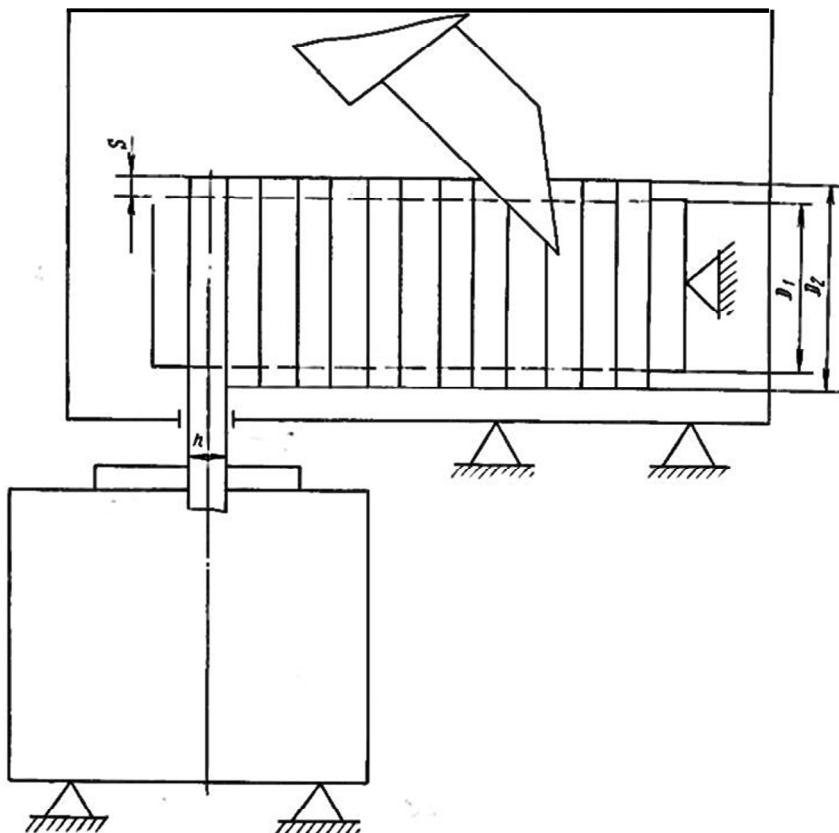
Схема изготовления разрезных колец из полимерного материала [2]
